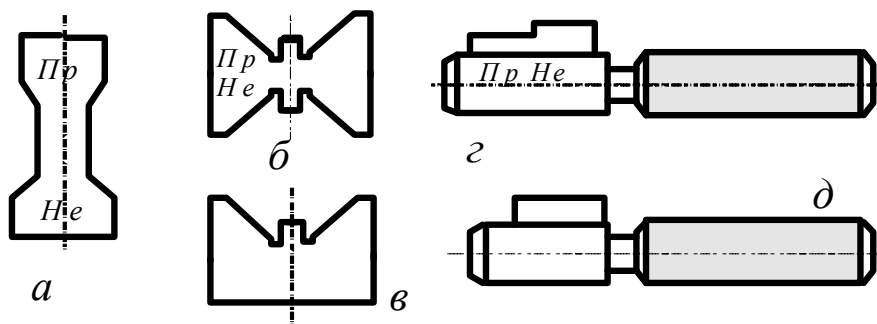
Калібри для контролю шпонкових з'єднань
